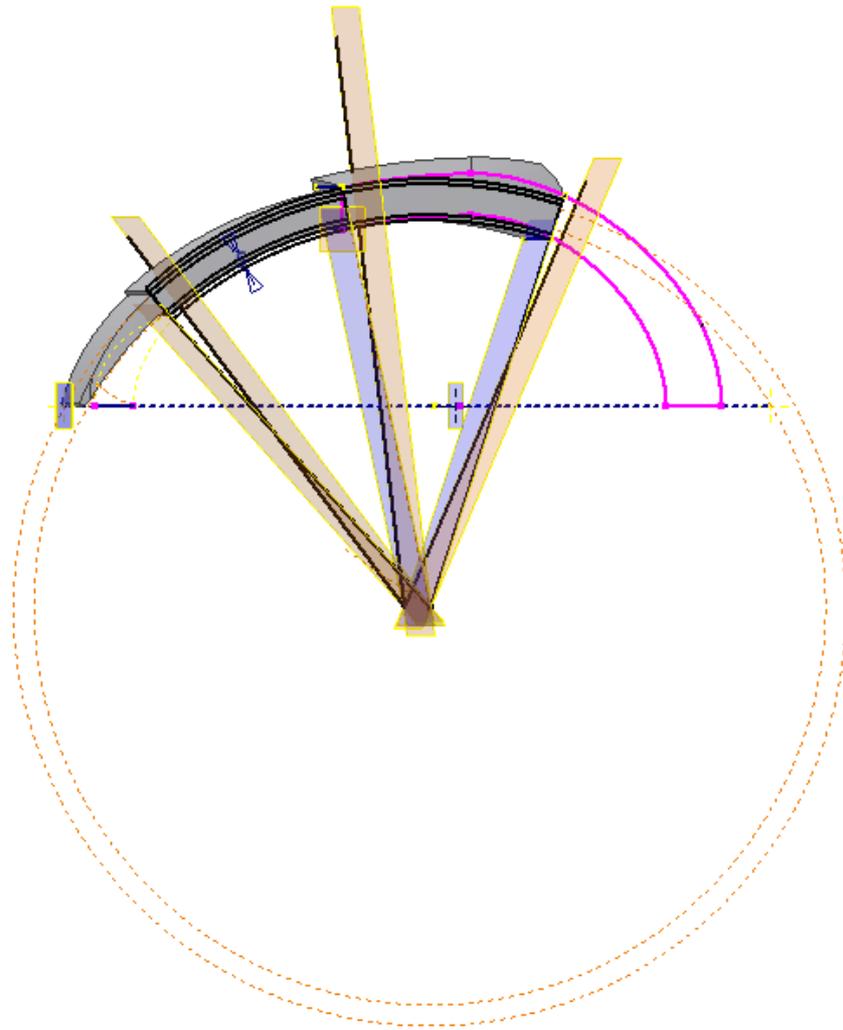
Construcción del modelo – prototipo. Vista inferior.
